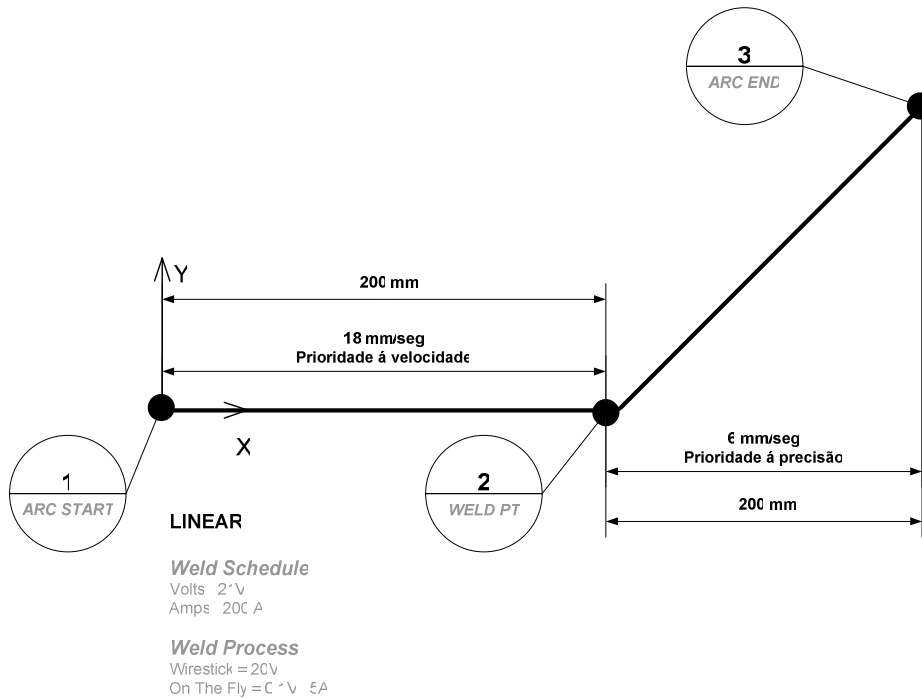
| Exercício 1 – Cordão de soldadura sobre uma linha
